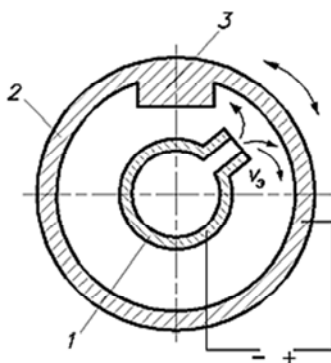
Схема точения при обработке части нежесткой заготовки:
